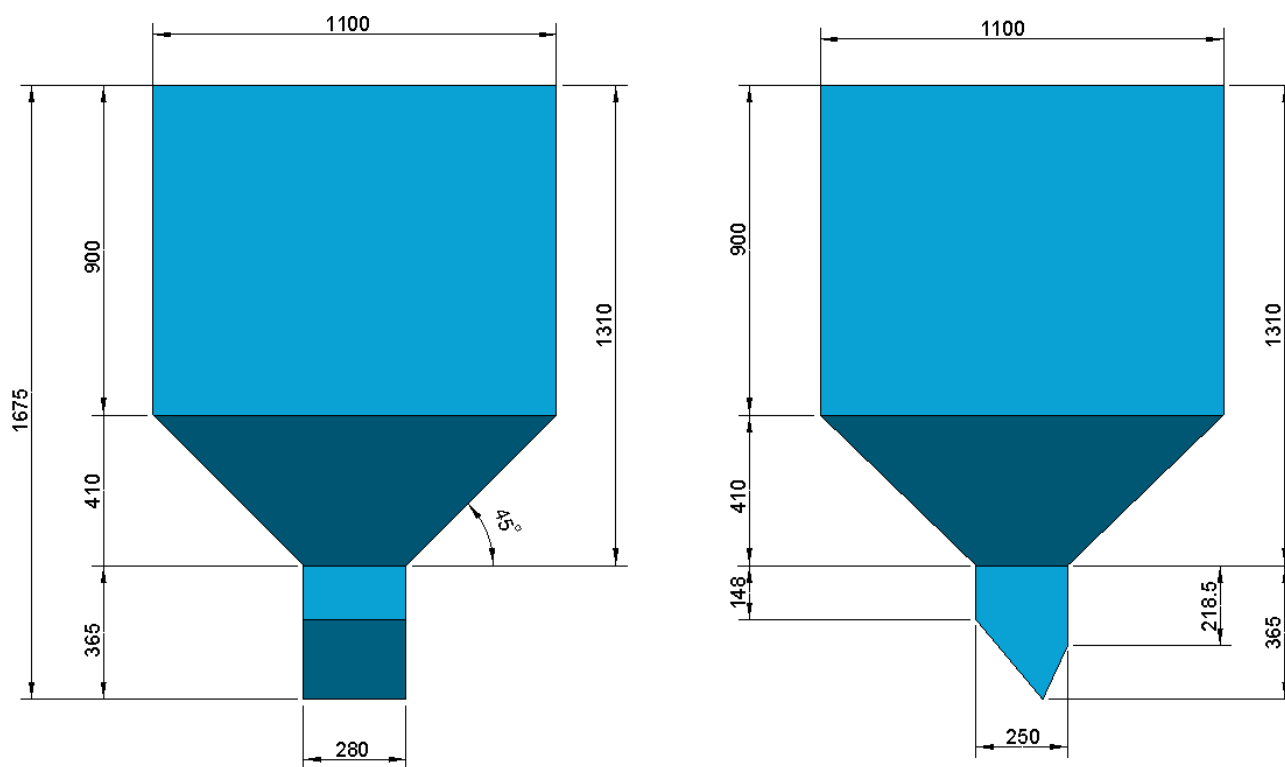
Definição da Geometria do Silo – Dimensões Internas
